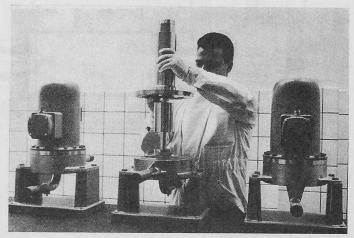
Pumpe mit Spaltrohrmotor für die Kern-Industrie. Nach einer sorgfältigen Reinigung werden die Pumpen unter Beachtung peinlichster Sauberkeit zusammengebaut
